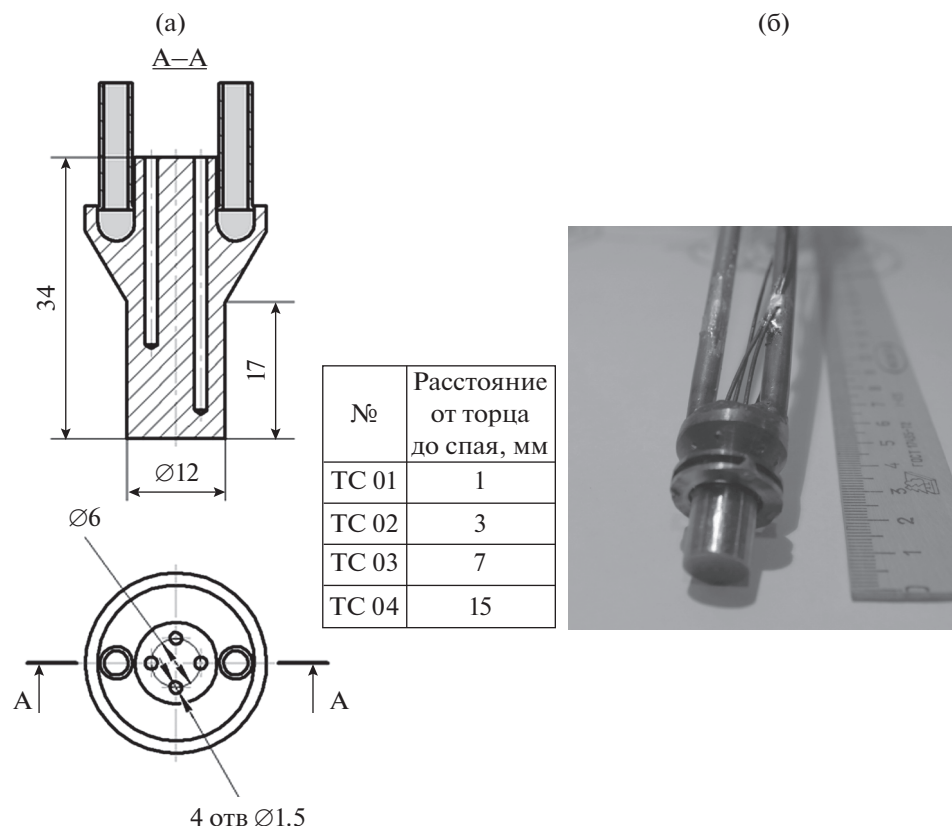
Погружаемый образец корпусной стали: (а) – сечение, вид сверху и схема размещения термопар; (б) – образец в сборе.
